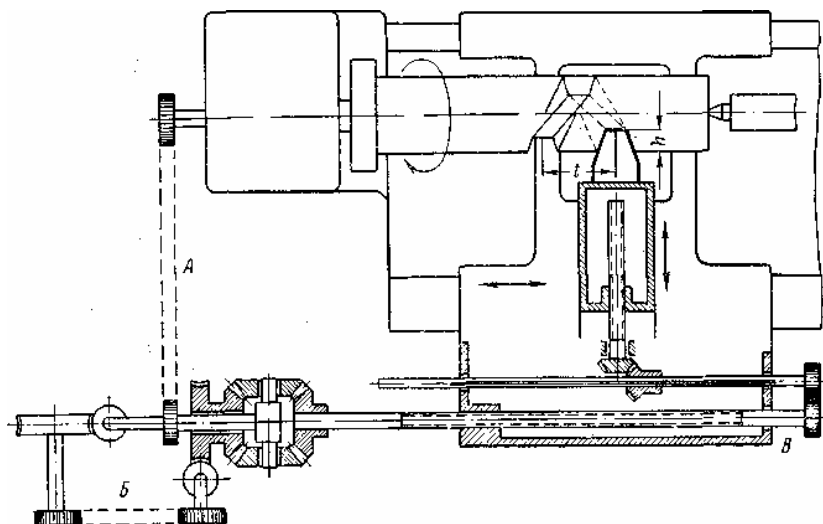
Компоновка станка для обработки винтов с переменным шагом
